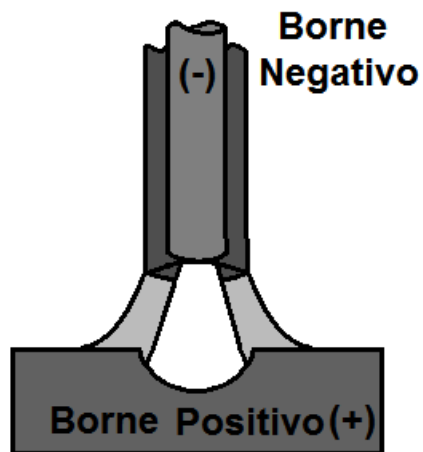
Polaridad directa en el proceso de soldadura SMAW.
